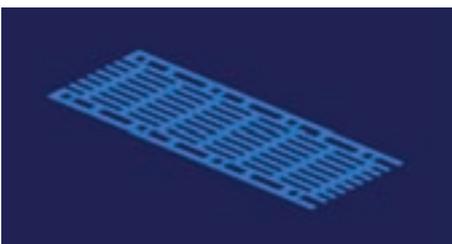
Blechlage vor dem Einlegen ins Werkzeug (Patentanmeldung Wilken/IWU)
